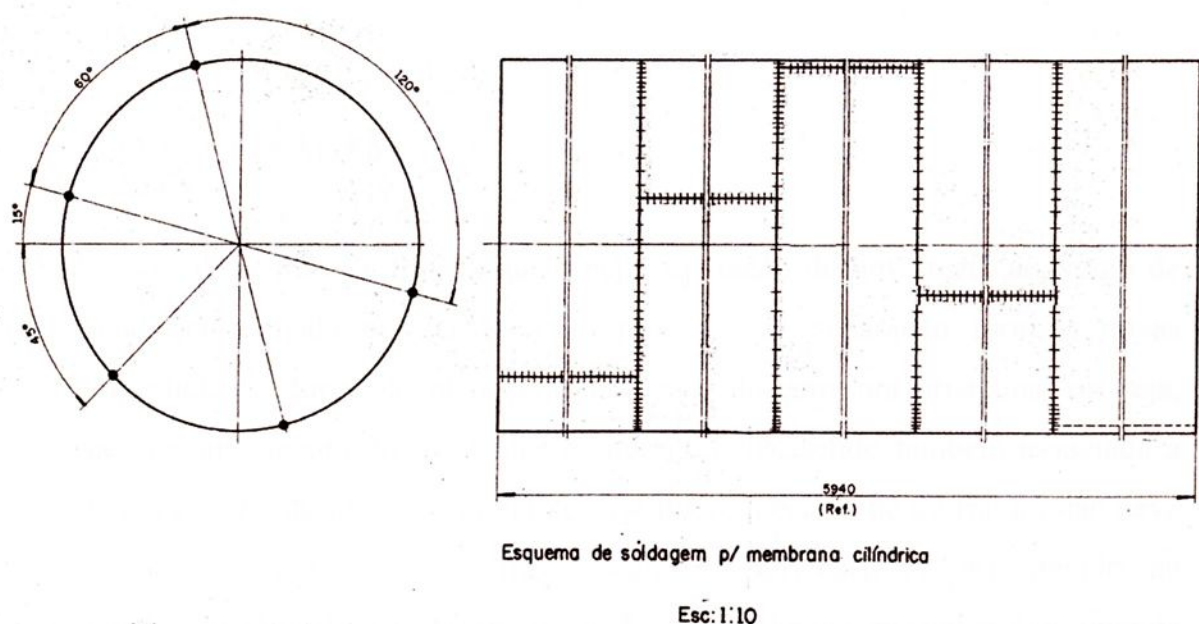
Esquema de soldagem das virolas para confecção de um Envelope Motor.
